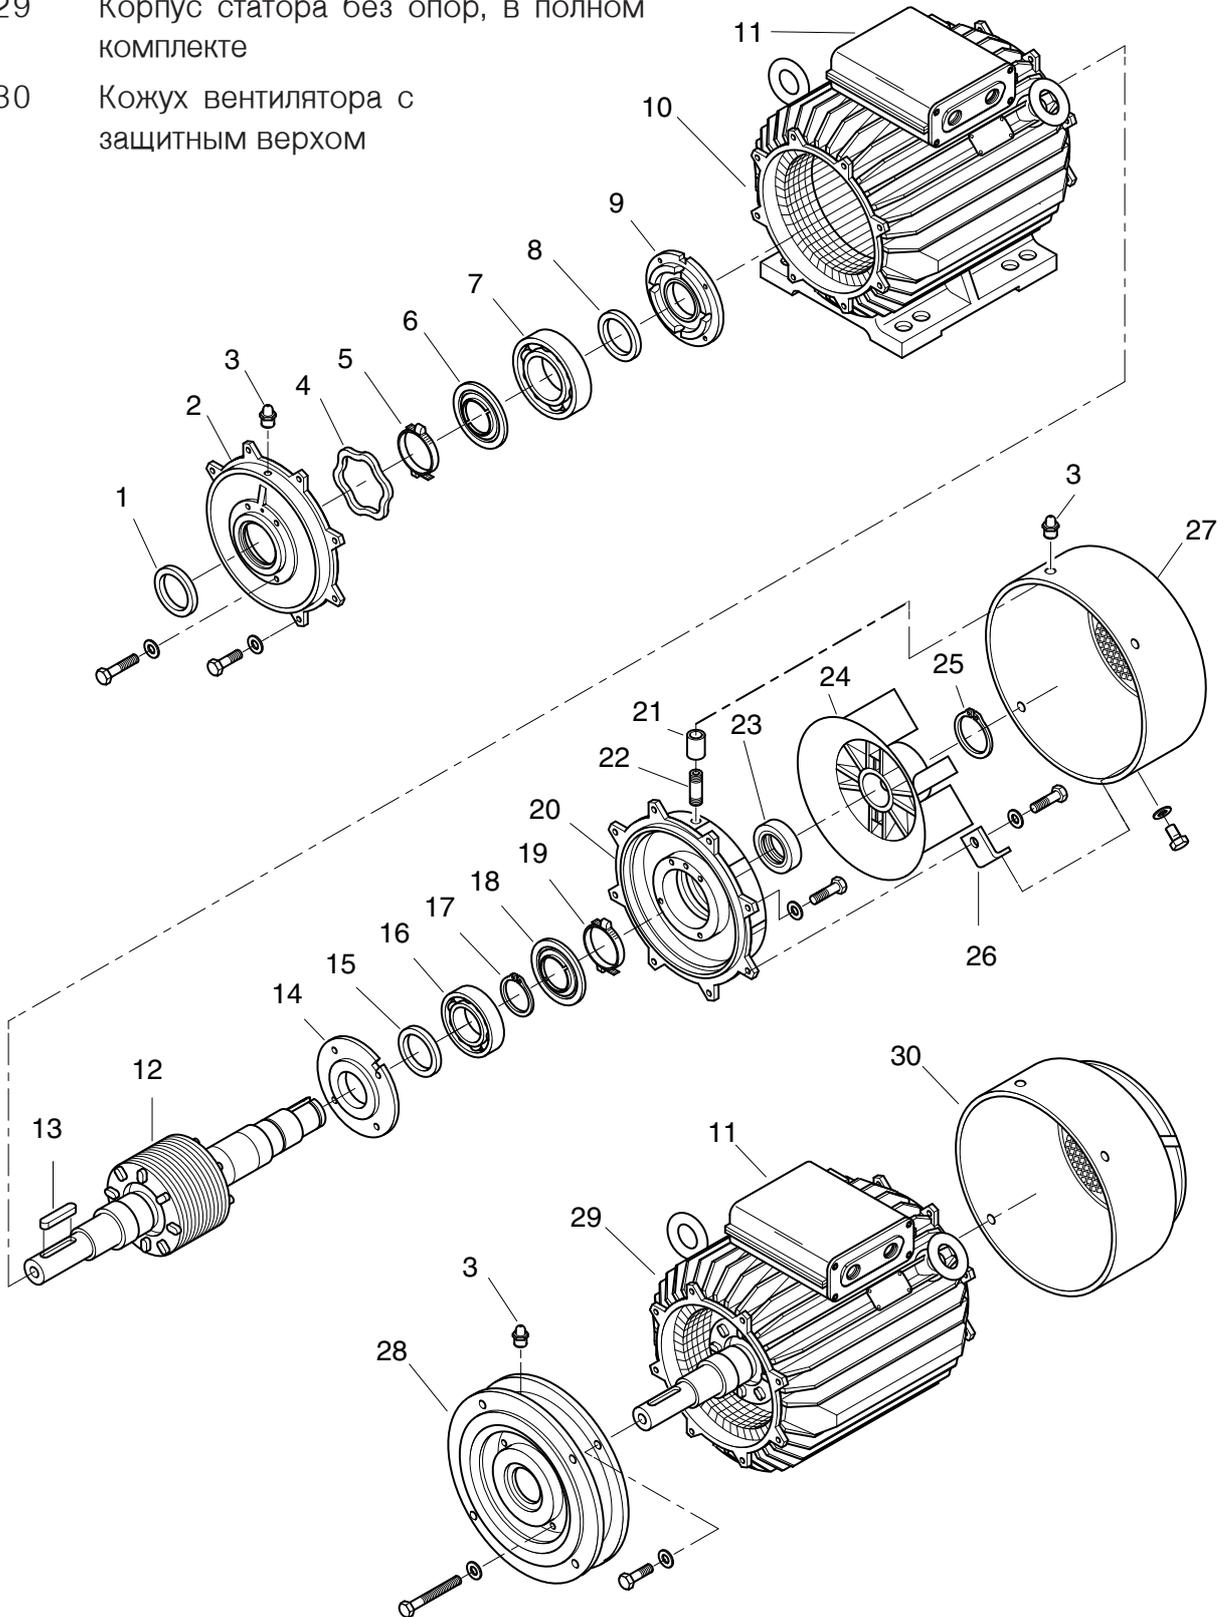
Развёрнутое изображение, IP55, типоразмер 180М-315L
